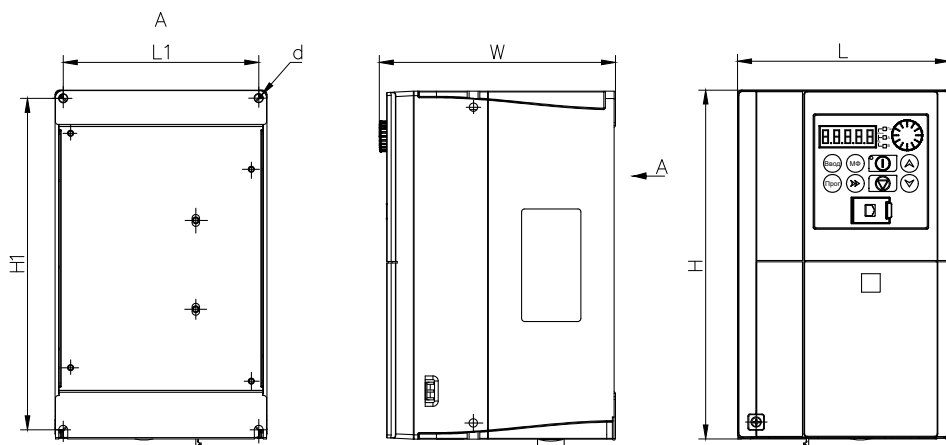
Габаритные и установочные размеры преобразователя (габариты 4–6)
